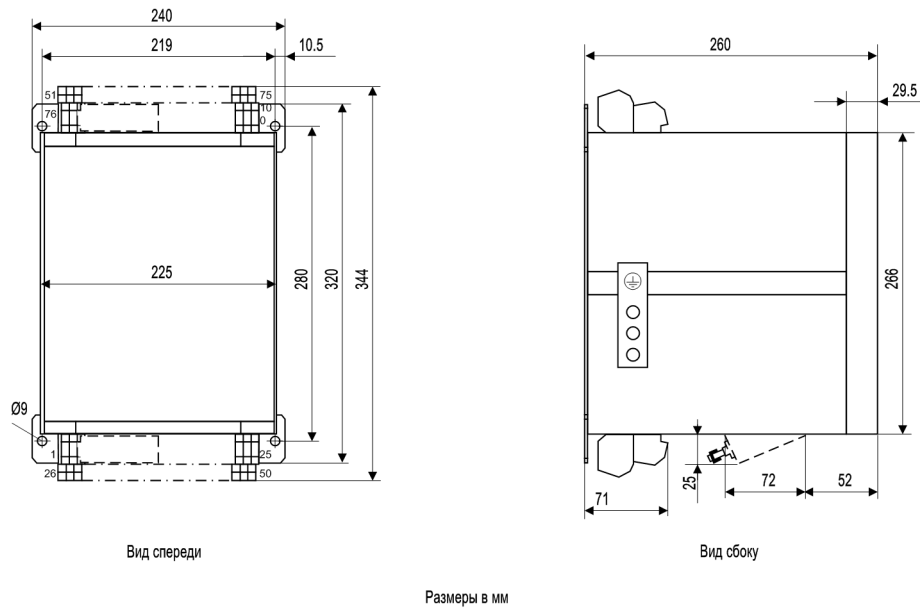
Размерные эскизы варианта устройства 7UM621 для навесного монтажа на панели (размер корпуса 1/2)
